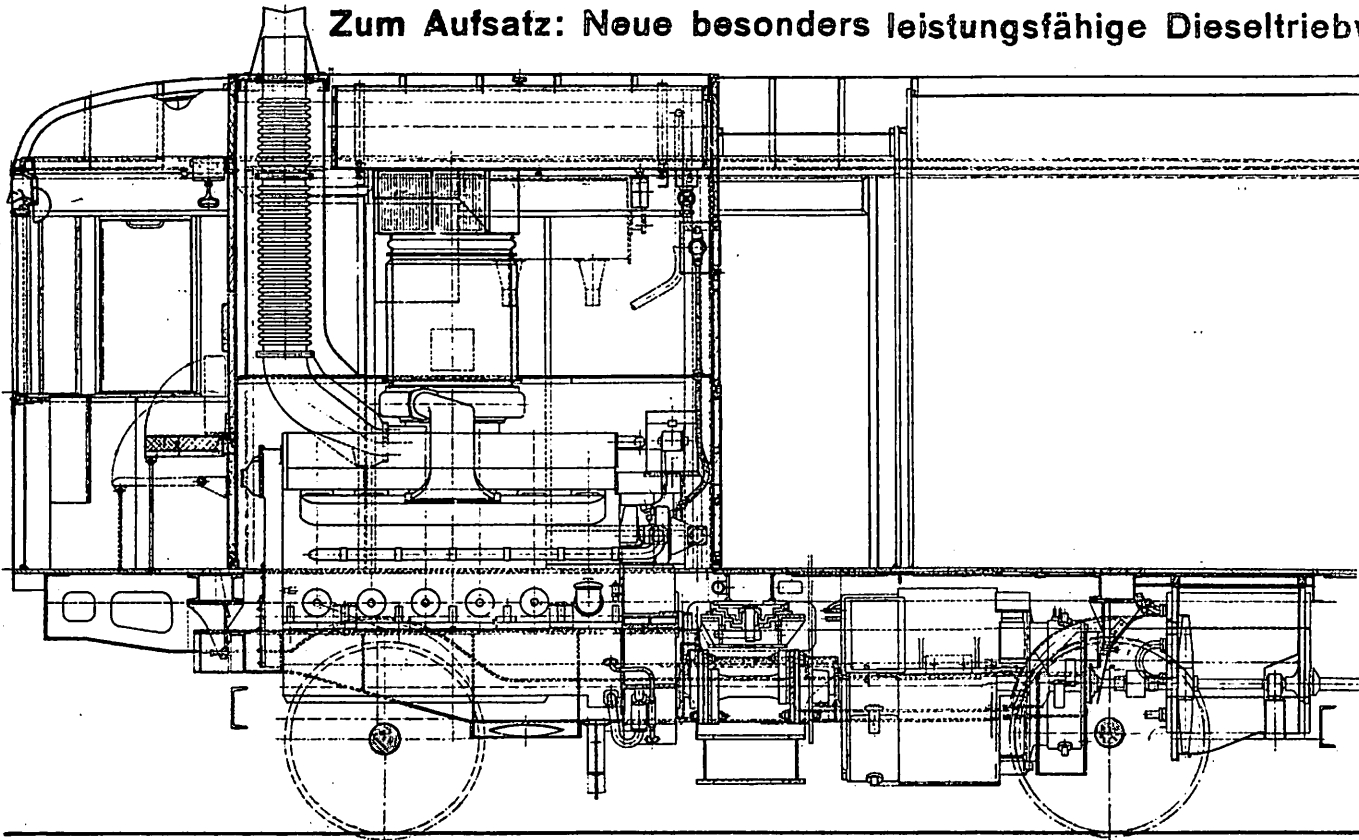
Längsschnitt durch den Maschinenraum. M. 1:36
